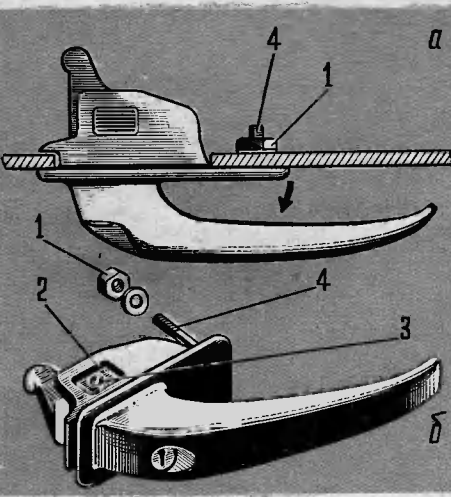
Ручка двери автомобиля ЗАЗ-965: а — крепление к наружной панели; б — извлечение цилиндра. 1 — гайка; 2 — окно; 3 — винт; 4 — шпилька. Стрелкой показано направление, в котором надо извлекать цилиндр.
